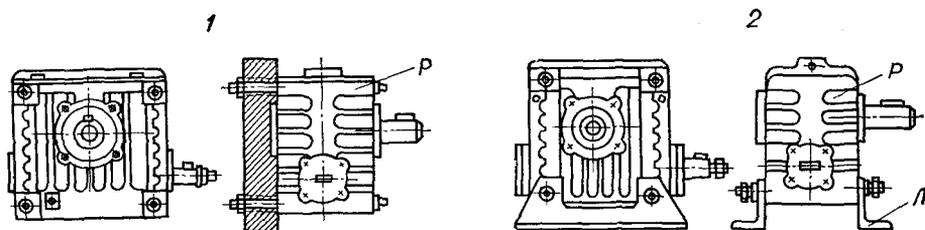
Способы крепления (1—2) редукторов РЧУ:
